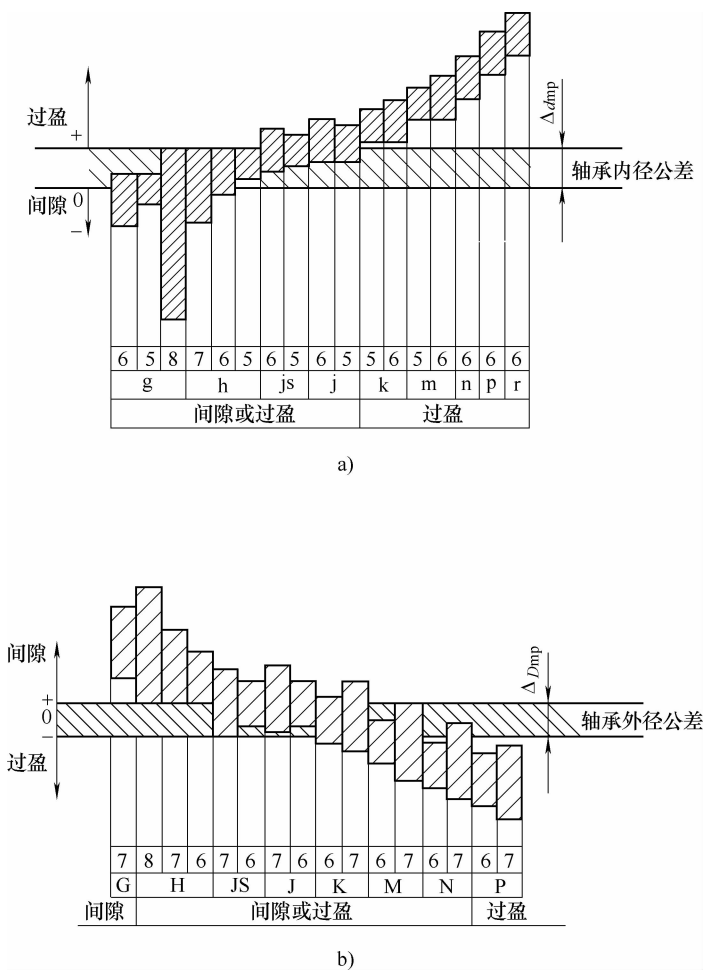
轴承与轴和外壳配合常用公差带
